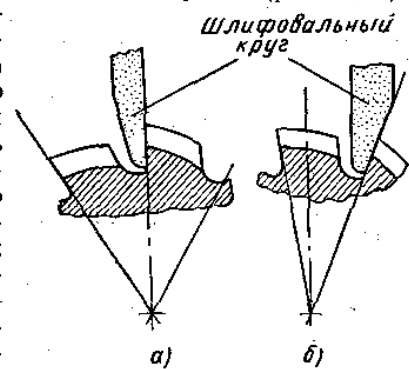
Заточка передней поверхности резьбовых фрез: а — с прямыми канавками, б — с винтовыми канавками
